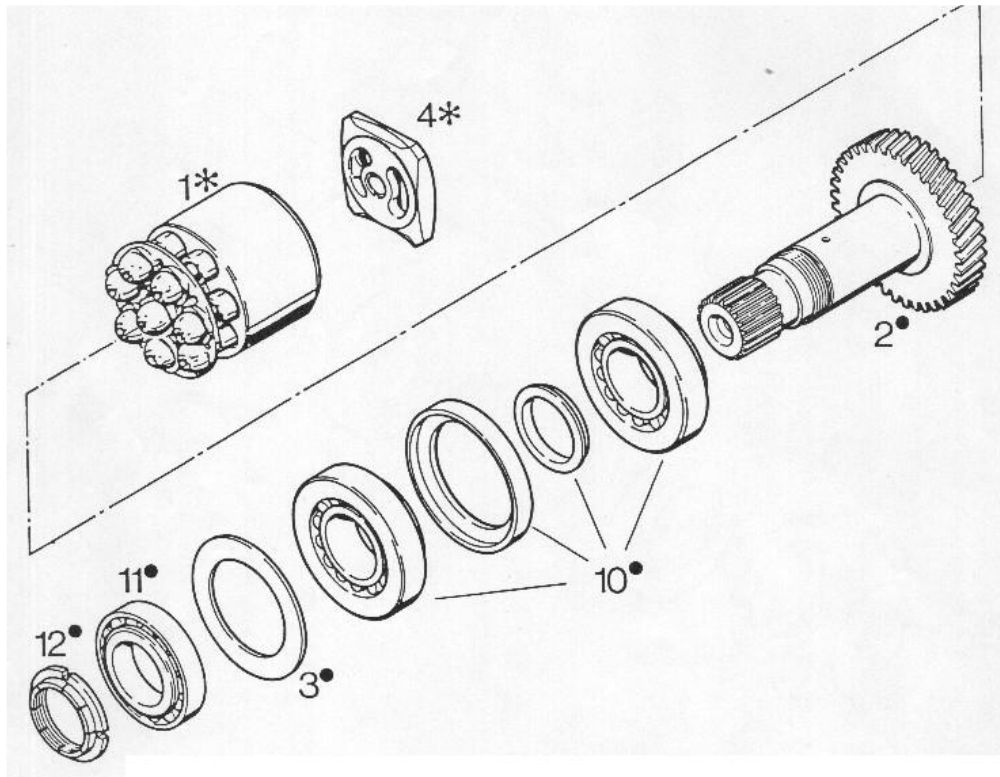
Vue éclatée de l'ensemble rotor hydrostatique2
